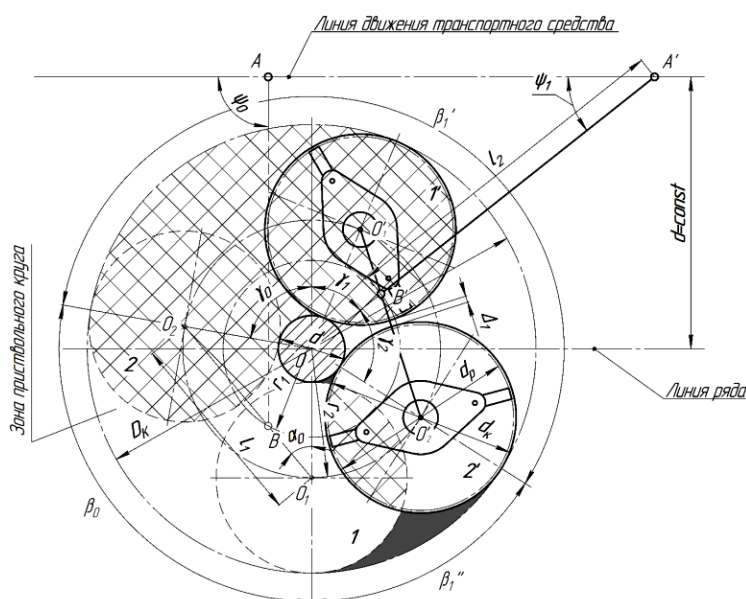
Конструктивно-кинематическая схема обхода штамба дерева рабочим органам фрезы
